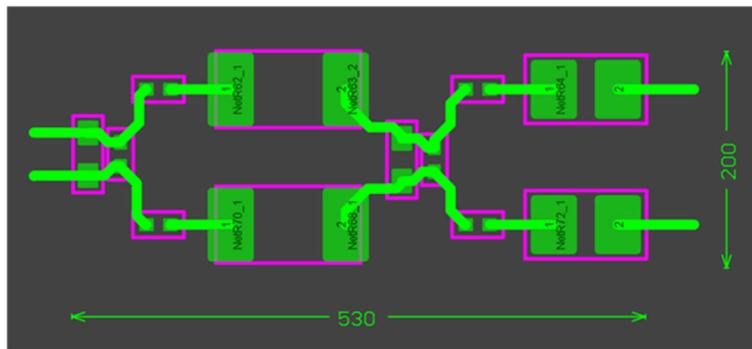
四阶模拟滤波器，PCB 或布局模型
